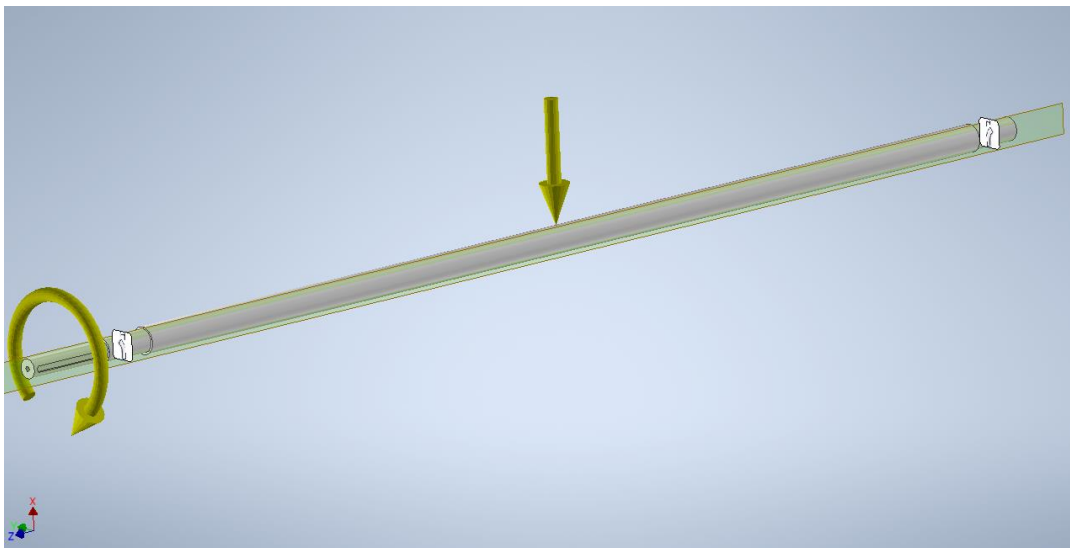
Detalle de las cargas aplicadas sobre el árbol.
